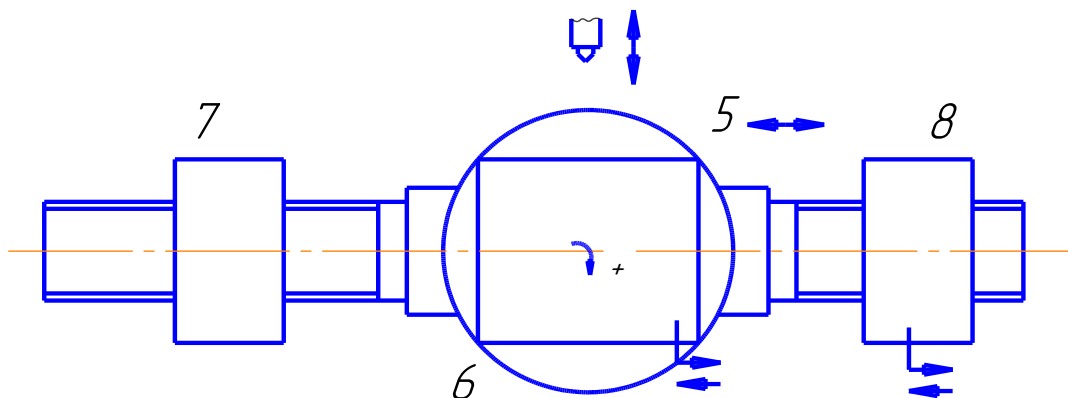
Компонувальна схема для кантування деталей.
